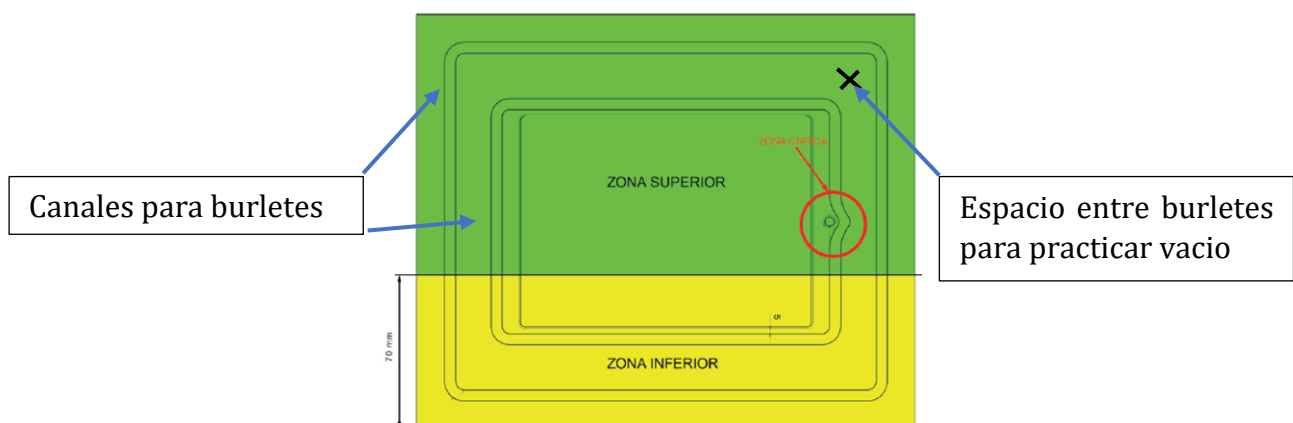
Figura K: Diseño de molde Aluminio (separación para fabricación en CNC)
